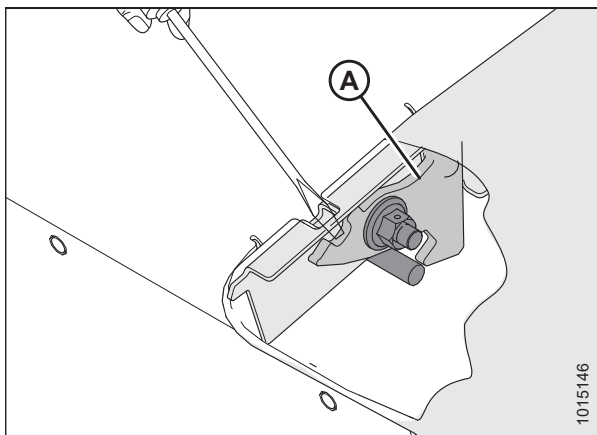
Защелка на щитке ножевого бруса — Местный разрез
